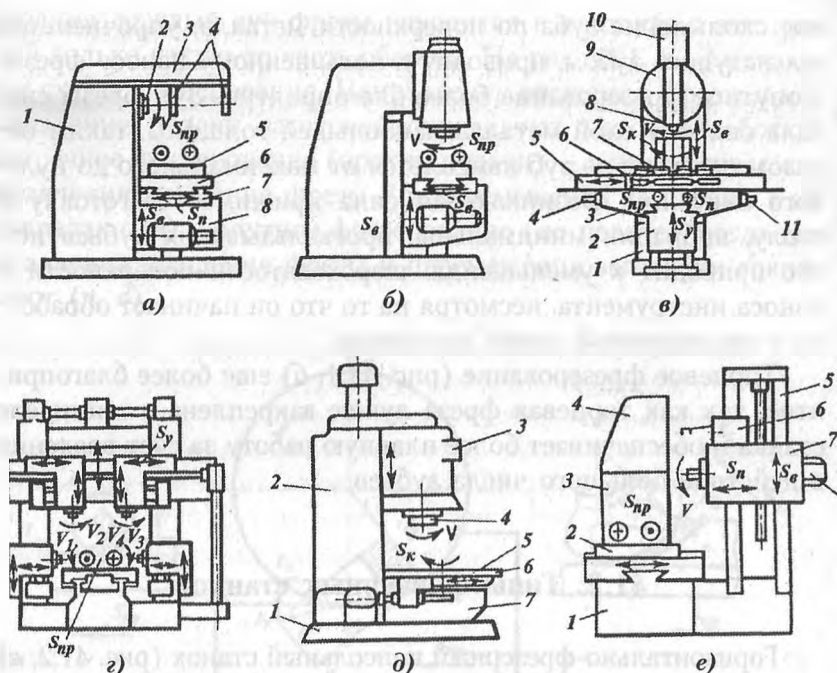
Типы фрезерных станков: а — горизонтально-фрезерный; б, в — вертикально-фрезерный; г — продольно-фрезерный; д — карусельно-фрезерный; е — копировально-фрезерный
